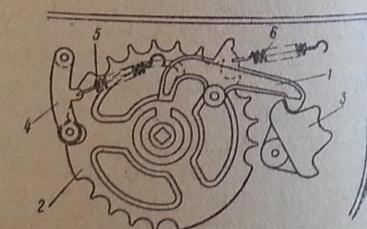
Блокирующий механизм контроллеров В-36 и В-30.
